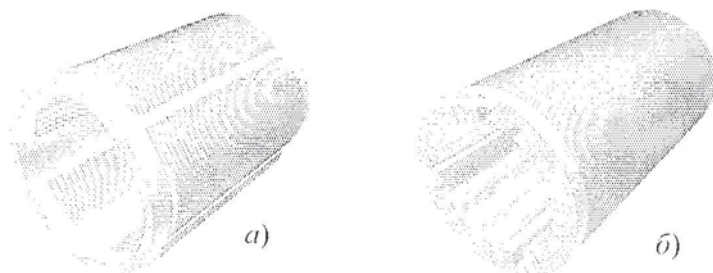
Конструкция щелевой фильтрующей трубы, полученная: *a* — из стандартной трубной заготовки, *б* — из трубной заготовки специального профиля
